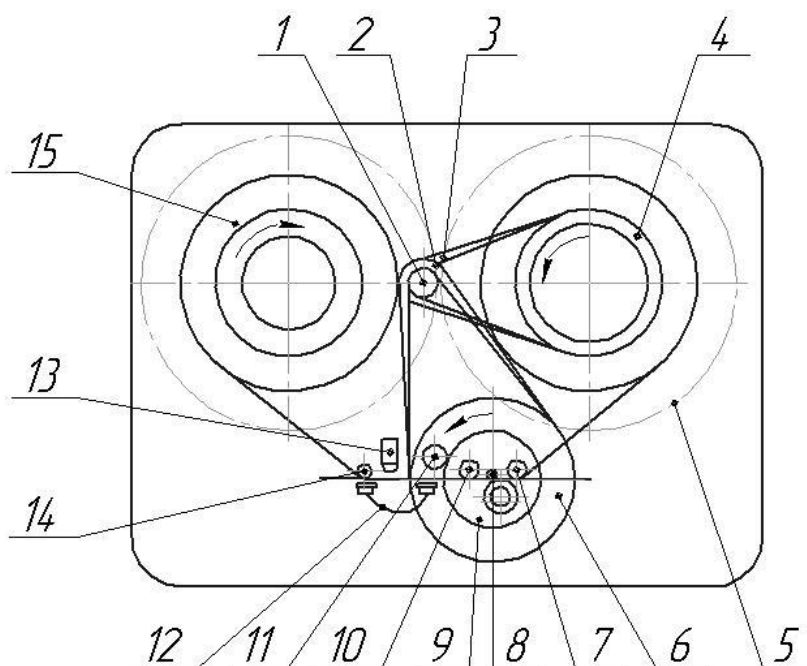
Кінематична схема стрічкопротяжного механізму
